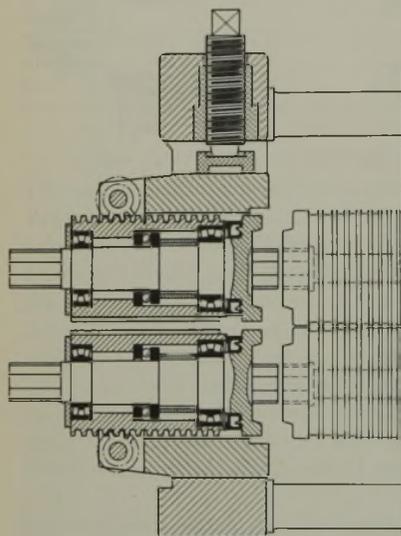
Rollenlager-Walzgerüst mit ausgefahrenem Rollenlager.
